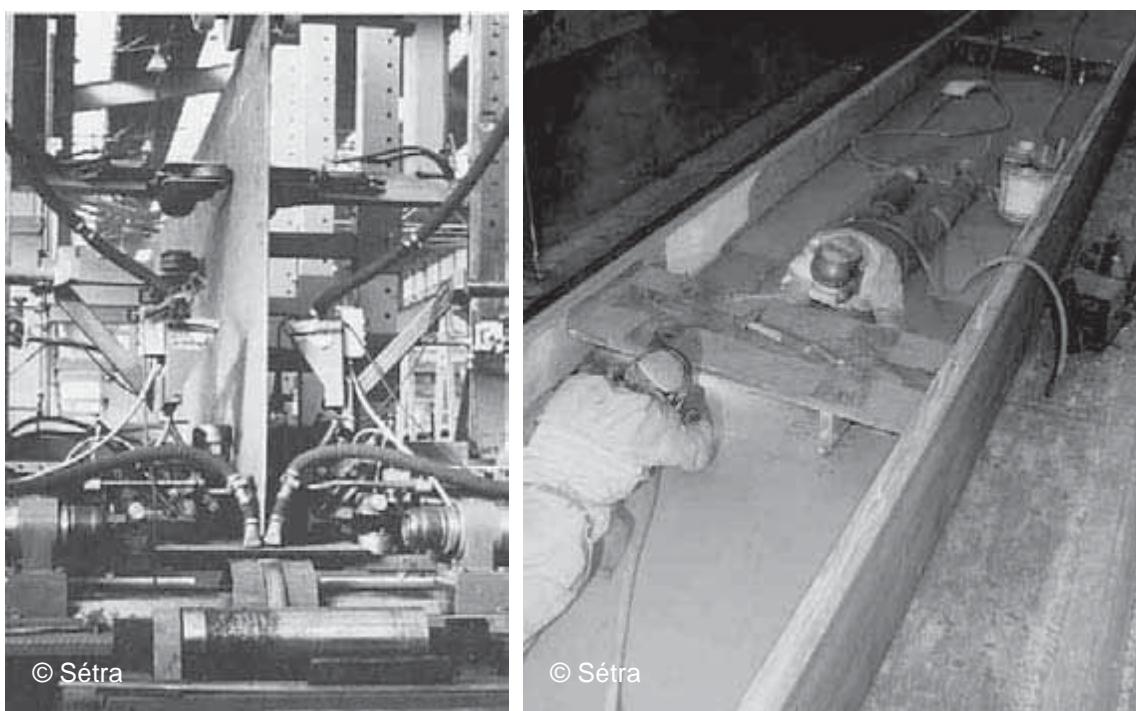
Reconstitution d'une poutre de pont en I et soudage de raidisseurs verticaux
